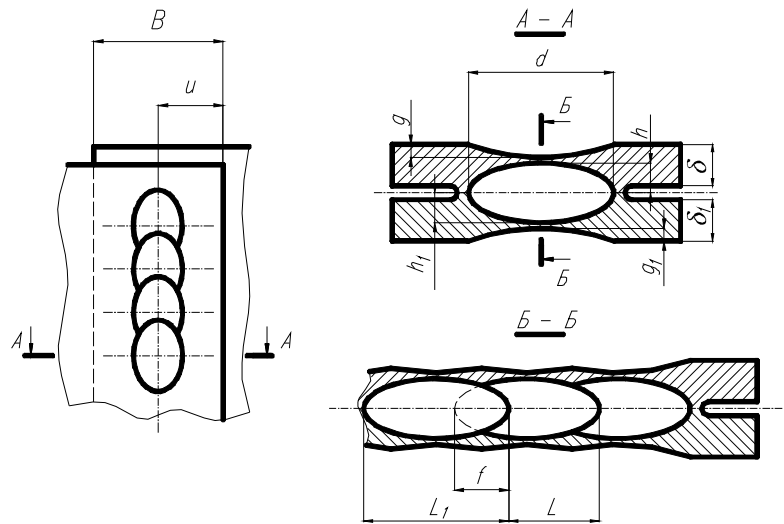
Параметри зварного з'єднання при контактному шовному зварюванні
